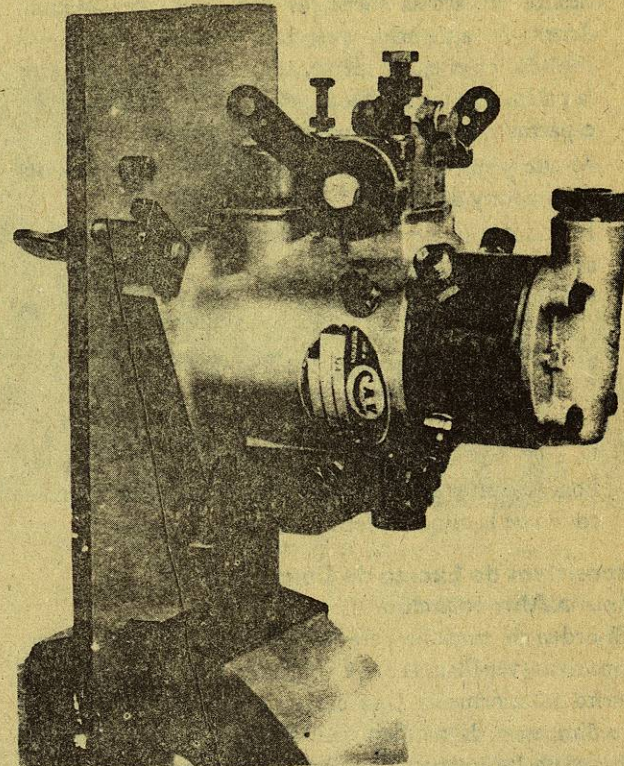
Regulador hidráulico de montaje reversible, puesto en el dispositivo de montaje y desmontaje
